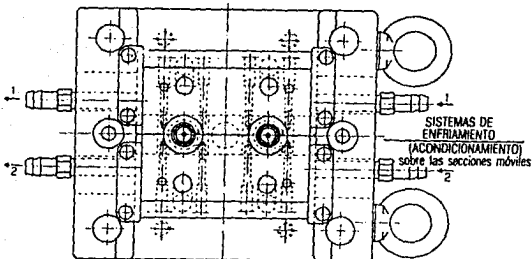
Sistema de refrigeración de un molde lado extractor [6].
